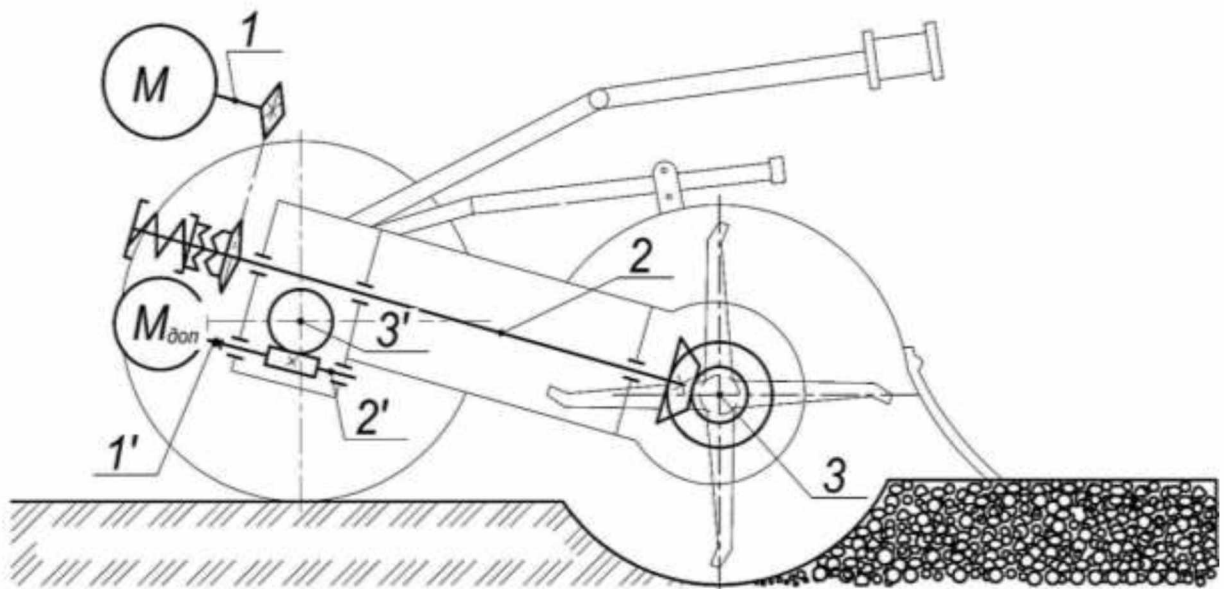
Кінематична схема ґрунтообробної фрези: 1 – вал основного двигуна; 2 – вал приводу робочих органів; 3 – вал робочих органів; 1' – вал додаткового двигуна; 2' – вал приводу ходових коліс; 3' – вал ходових коліс
